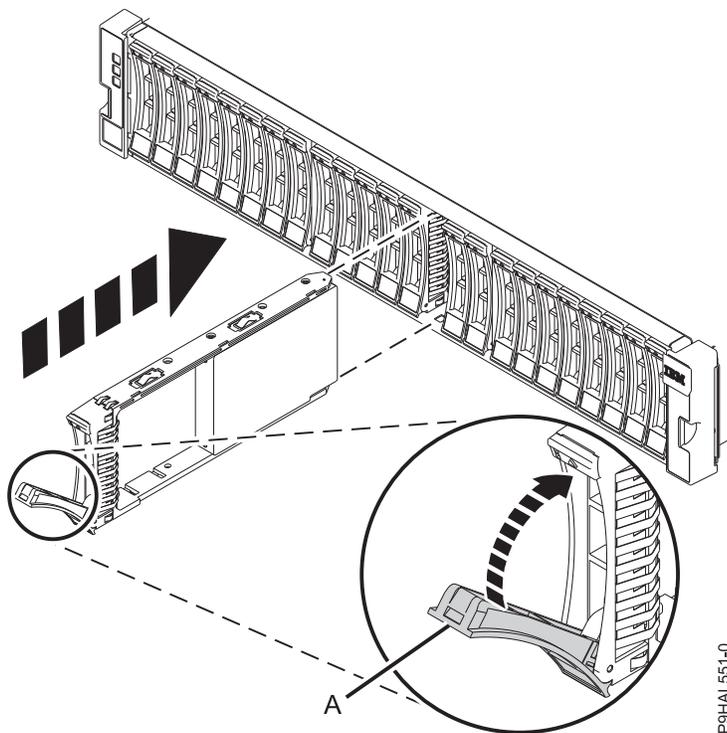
Laufwerk im Plattenlaufwerkgehäuse installieren
